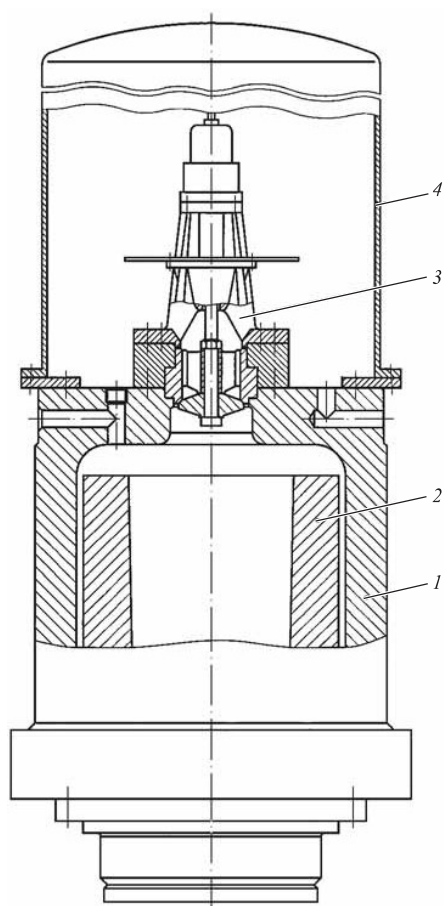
Конструктивная схема системы наполнения рабочего гидроцилиндра штамповочного пресса Н-220-80-D силой 20 МН ("СМС CLEARING HYDRAULIK"):
